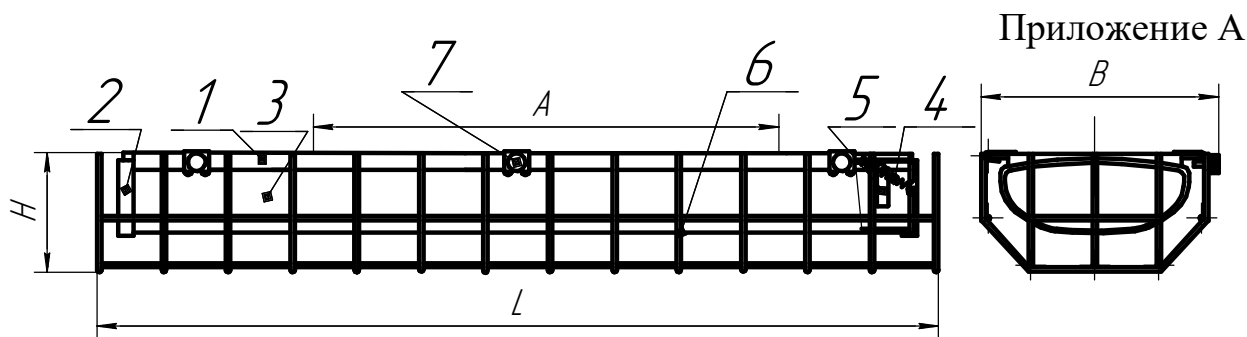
1. Корпус в сборе, 2. Крышка, 3. Рассеиватель, 4. Пружина, 5. Патрон, 6. Решетка, 7. Винт специальный.
